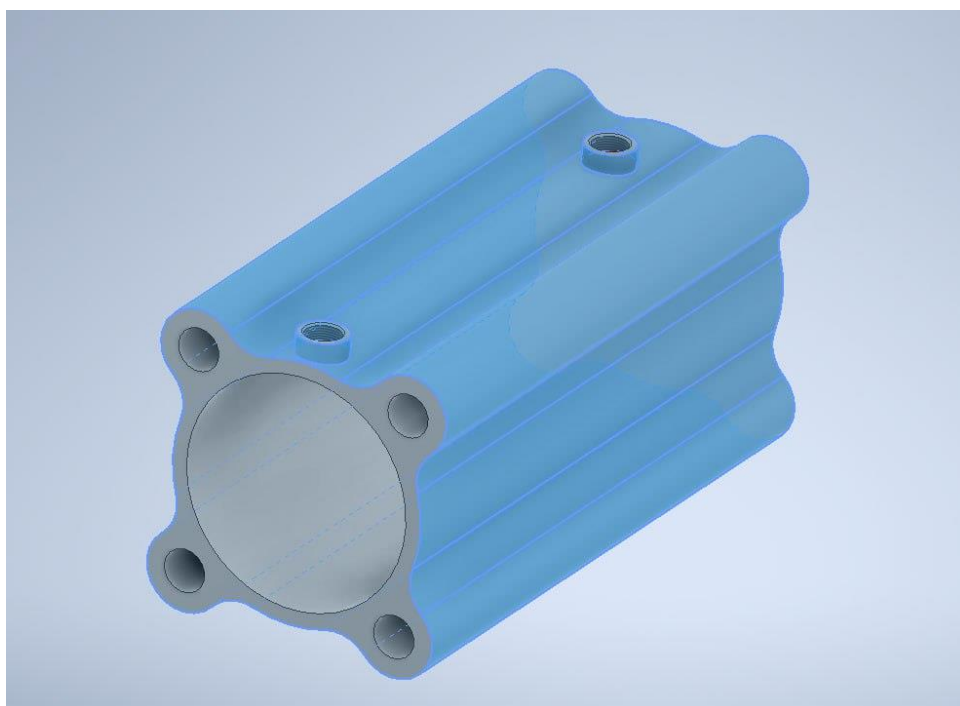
Обробка корпусу на фрезувальному верстаті
